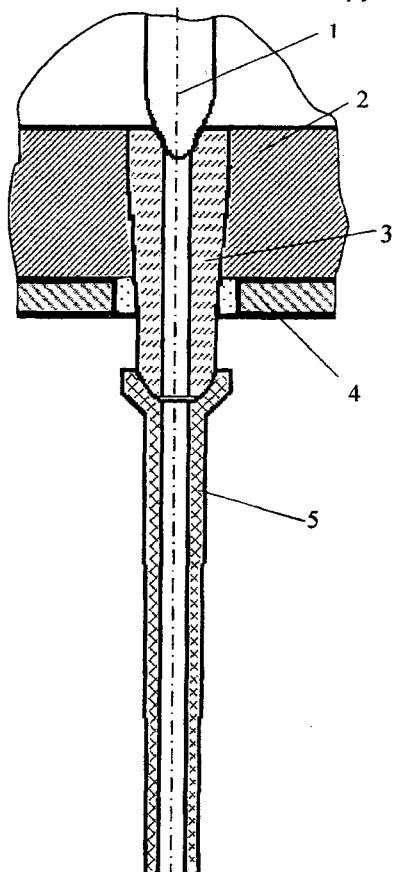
Схема разливочного узла промежуточного ковша сортовой МНЛЗ:
